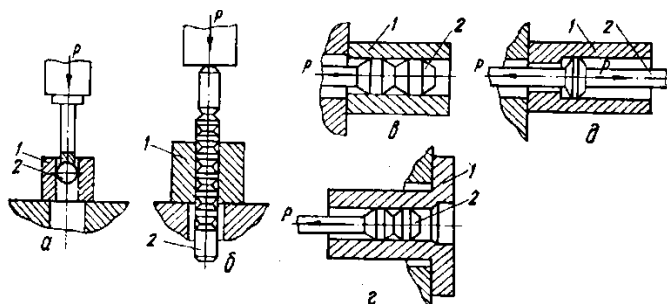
Схеми протягування отворів: а, б – прошовхуванням кульки й протягування на пресах; в, г – калібруванням зі стиском і розтяганням деталі на горизонтально-протяжному верстаті; д – калібруванням при зворотньо-поступальному ході протягування на спеціальних верстатах; 1 – деталь; 2 – інструмент
